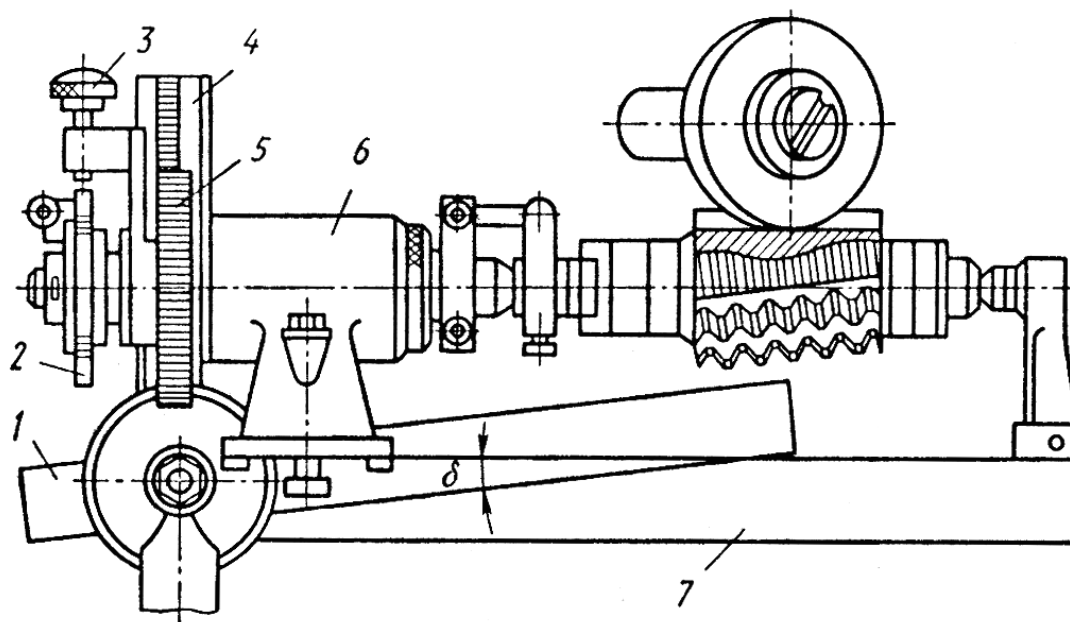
Приспособление для заточки червячных фрез на универсально-заточном станке:
